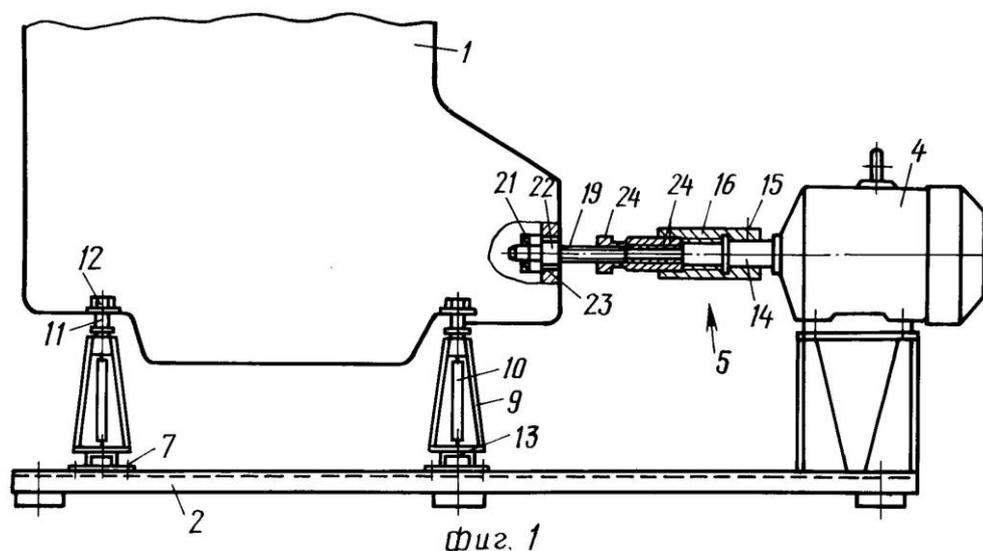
Стенд для обкатки ДВС грузовых автомобилей
